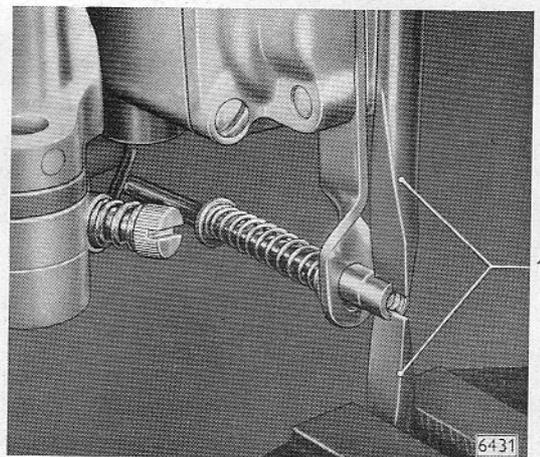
Gewinde der Pumpenverbindungsstange verstemmen
